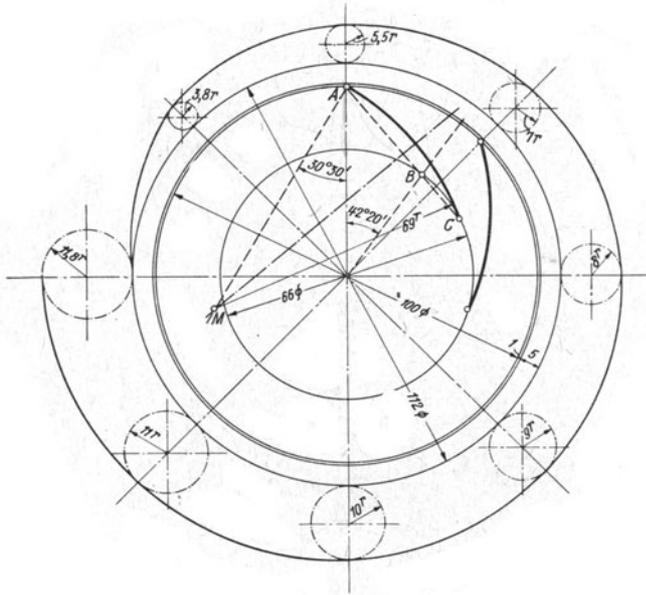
Entwurfsgrundlage für Spirale und Laufrad einer Kühlwasserpumpe.
